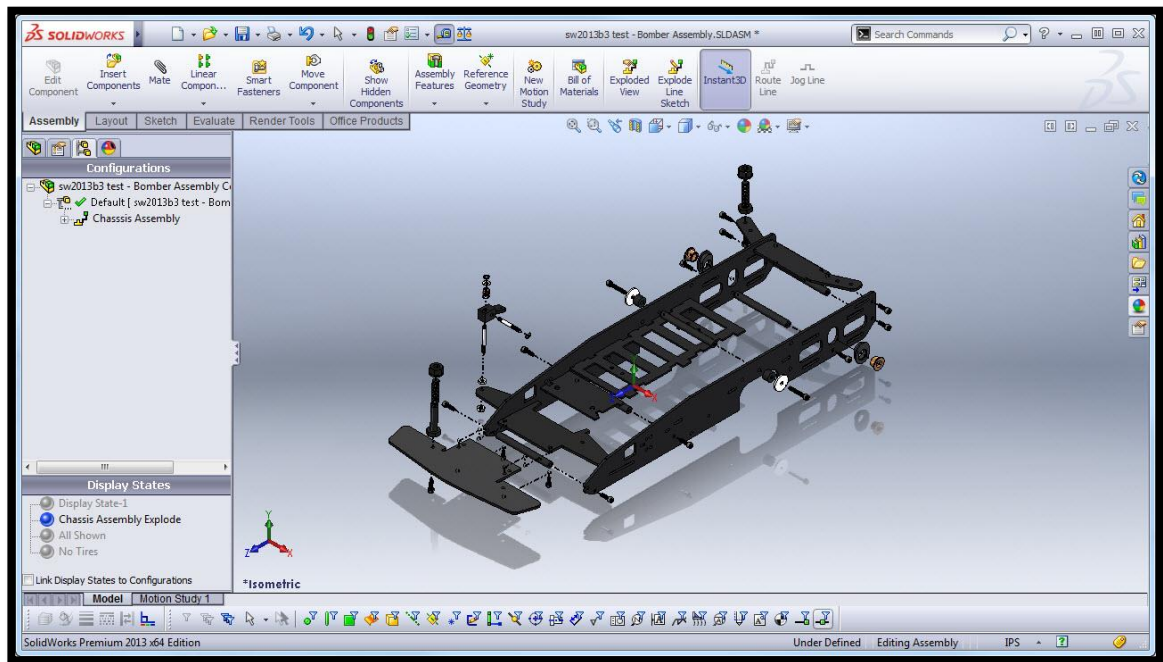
En SolidWorks 2013 permite la vista explosionada de la pieza diseñada.
